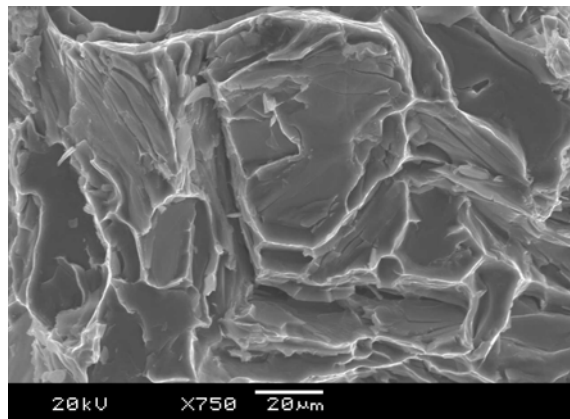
Aspecto da superfície na região da fratura do corpo de prova de tração no estado bruto de fundição.
